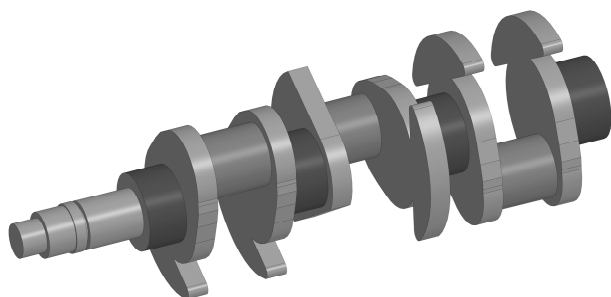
Коленчатый вал двигателя ЯМЗ-236 производства ПАО «Автодизель»
